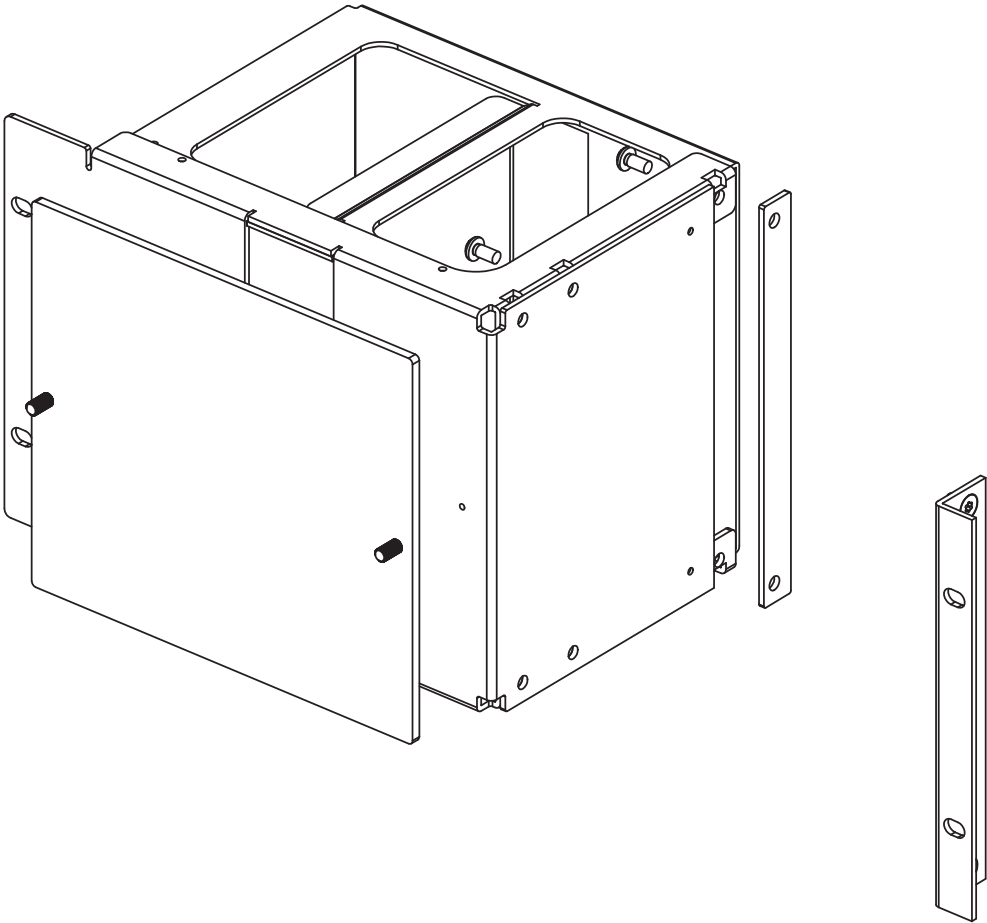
Soporte de montaje de 4U para dispositivo de prueba
